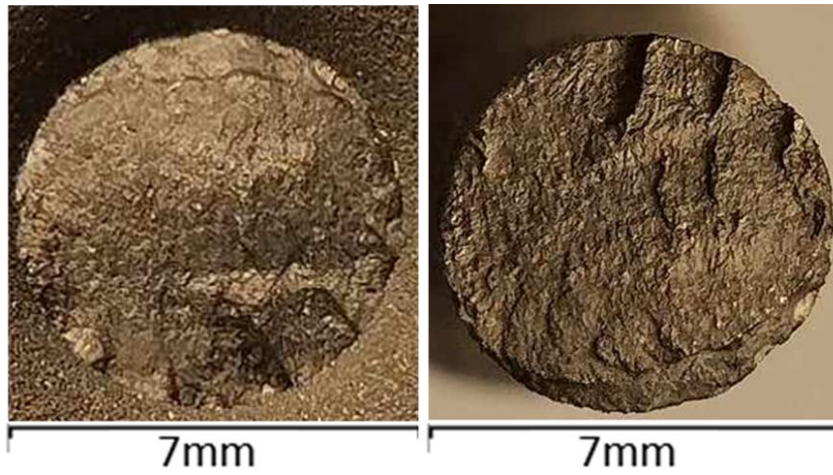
Superfície de fratura macroscópica do provete L4F1.
